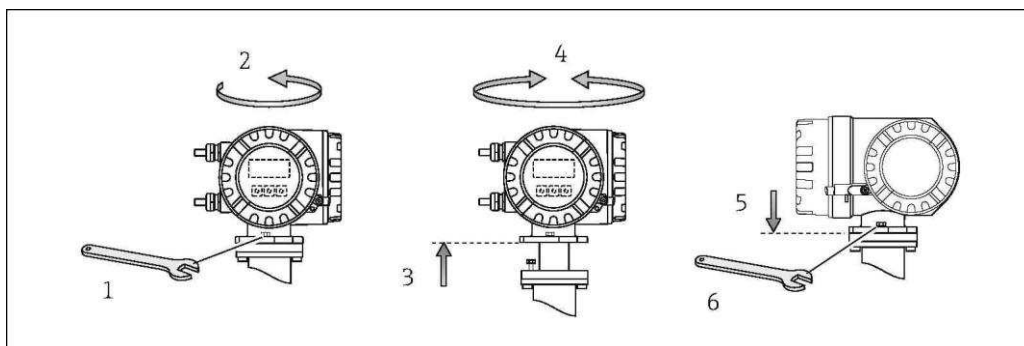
Вращение корпуса трансмиттера (алюминиевый полевой корпус)
